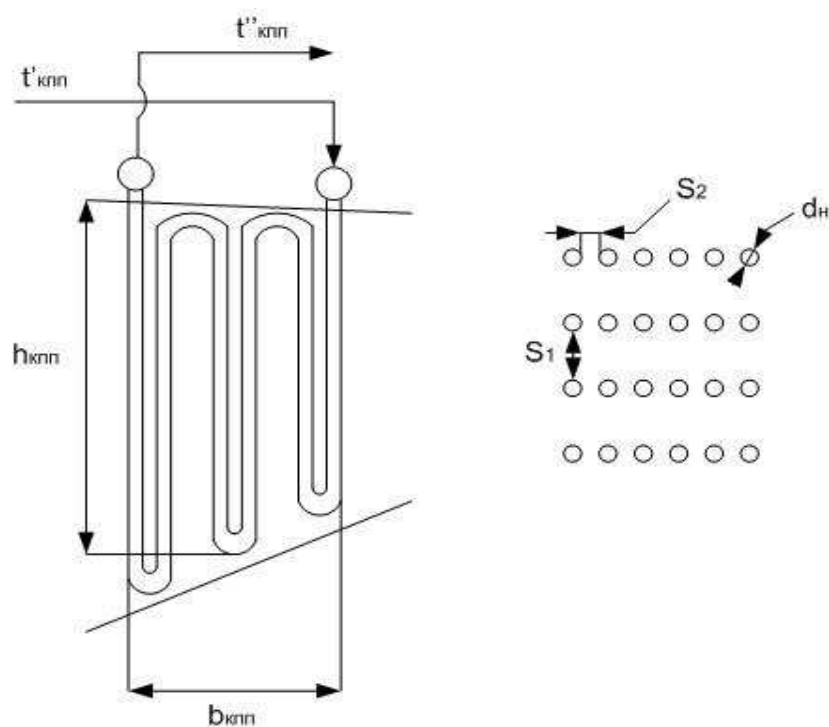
Конструктивные размеры конвективного пароперегревателя
